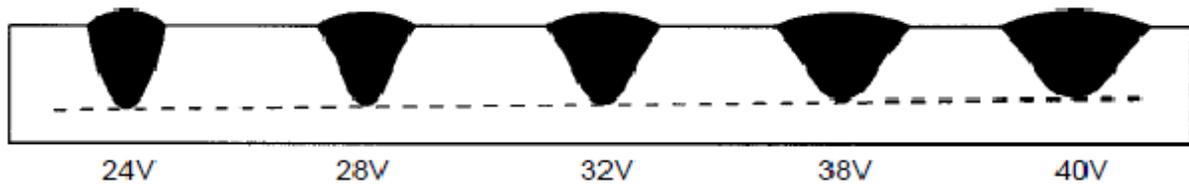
Effet de la tension d'arc sur l'aspect de la soudure.
